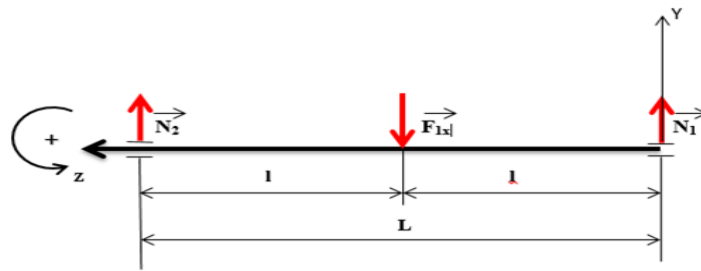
bilan des forces d'axe d'articulation segment 1/2 plan horizontal
